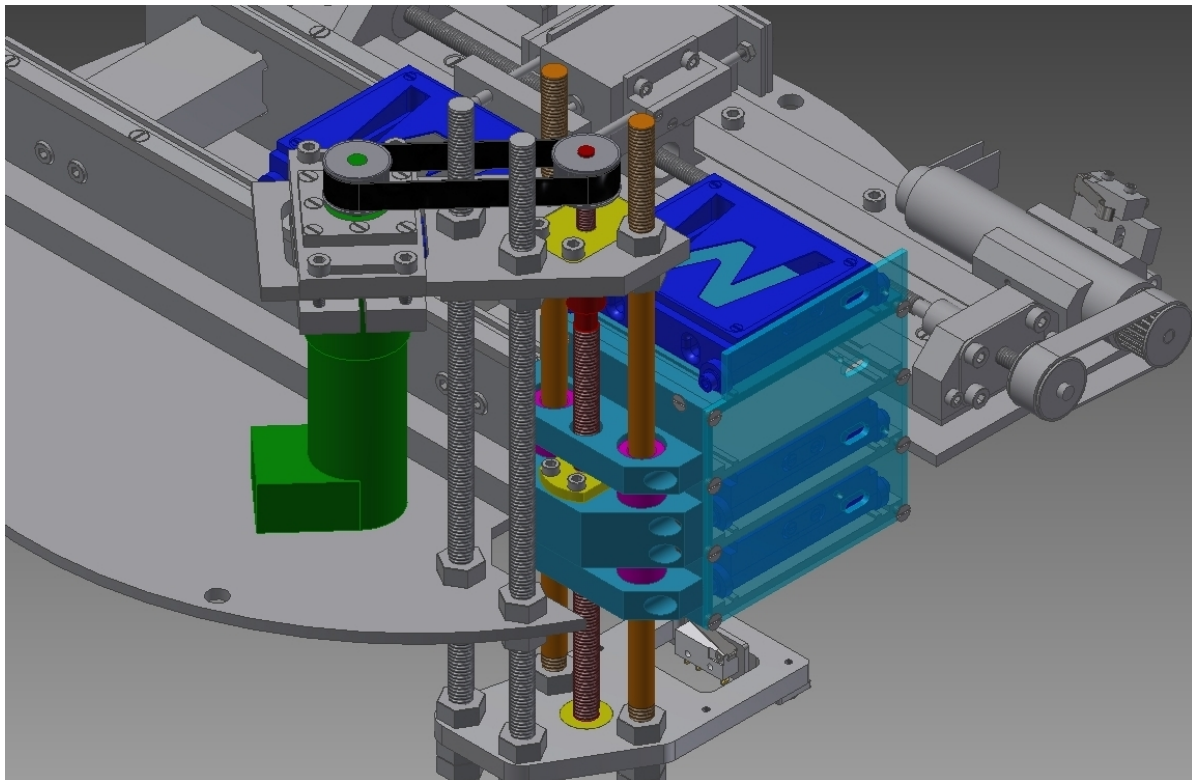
Detailansicht des Magazins des Maskensystems. Die Position des Maskenmagazins (türkis) wird über die Kugelgewindestange (rot mit gelben Lagern) eingestellt und mittels Zahnriemen (schwarz) über den Schrittmotor (grün) angetrieben. Dabei ist das Magazin mit Linearkugellagern (magenta) an zwei Führungsstangen (orange) gegen Verkippen gesichert. Material: Edelstahl, Aluminium. Abmessungen: 245 mm x 330 mm x 331 mm.
